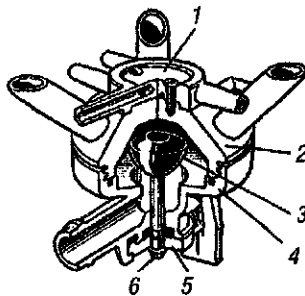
Схема коллектора: 1 – распределитель; 2 – корпус; 3 – резиновый клапан; 4 – крышка; 5 – резиновая шайба; 6 – шплинт
